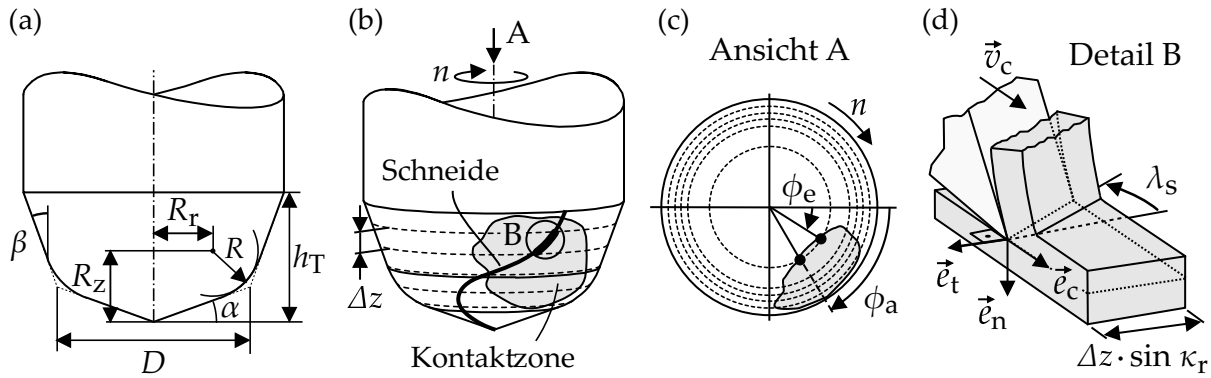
Werkzeugparametrierung beliebiger Schaftwerkzeuge nach [EA01] (a), Werkzeugsegmentierung und Kontaktzone beim Fräsen nach [LBE11] (b,c) und lokales Koordinatensystem am Schneidenelement in Anlehnung an [Sur06] (d)
